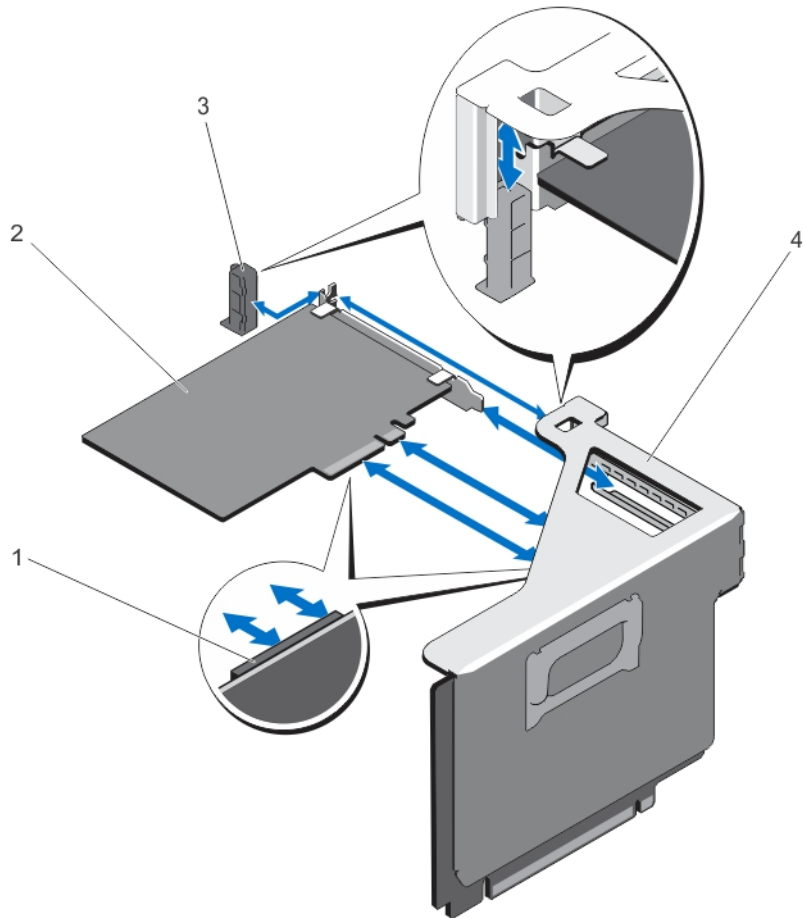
Retrait et installation de la carte d'extension (demi-longueur) à partir de la carte de montage 2 pour carte d'extension
